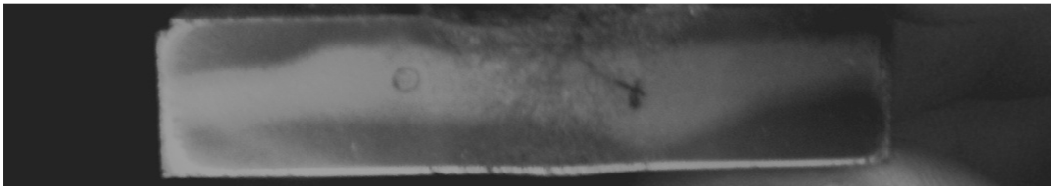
64 - Amostra do provete 4 (soldadura com vibração).
